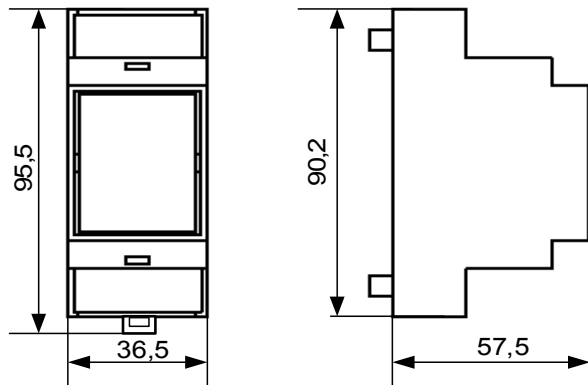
Габаритные и присоединительные размеры преобразователя
